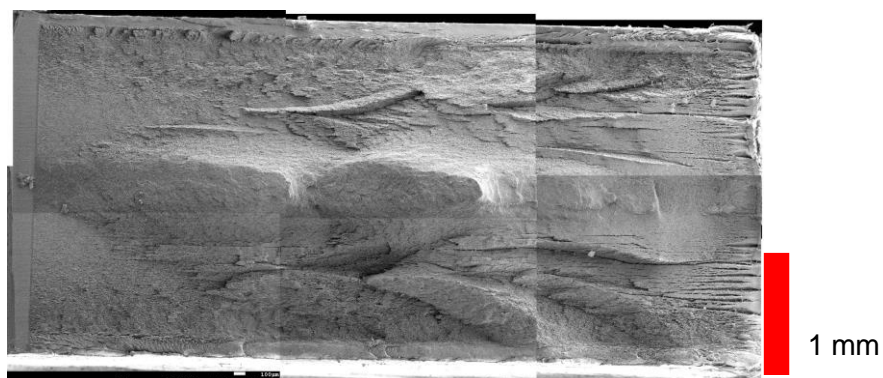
Imatge composta de la superfície de fractura de Bioblend 3 zona lateral
